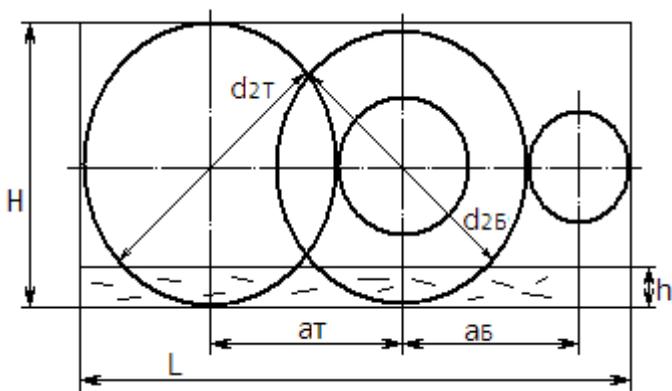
Двухступенчатые редукторы с развернутой и раздвоенной схемами
